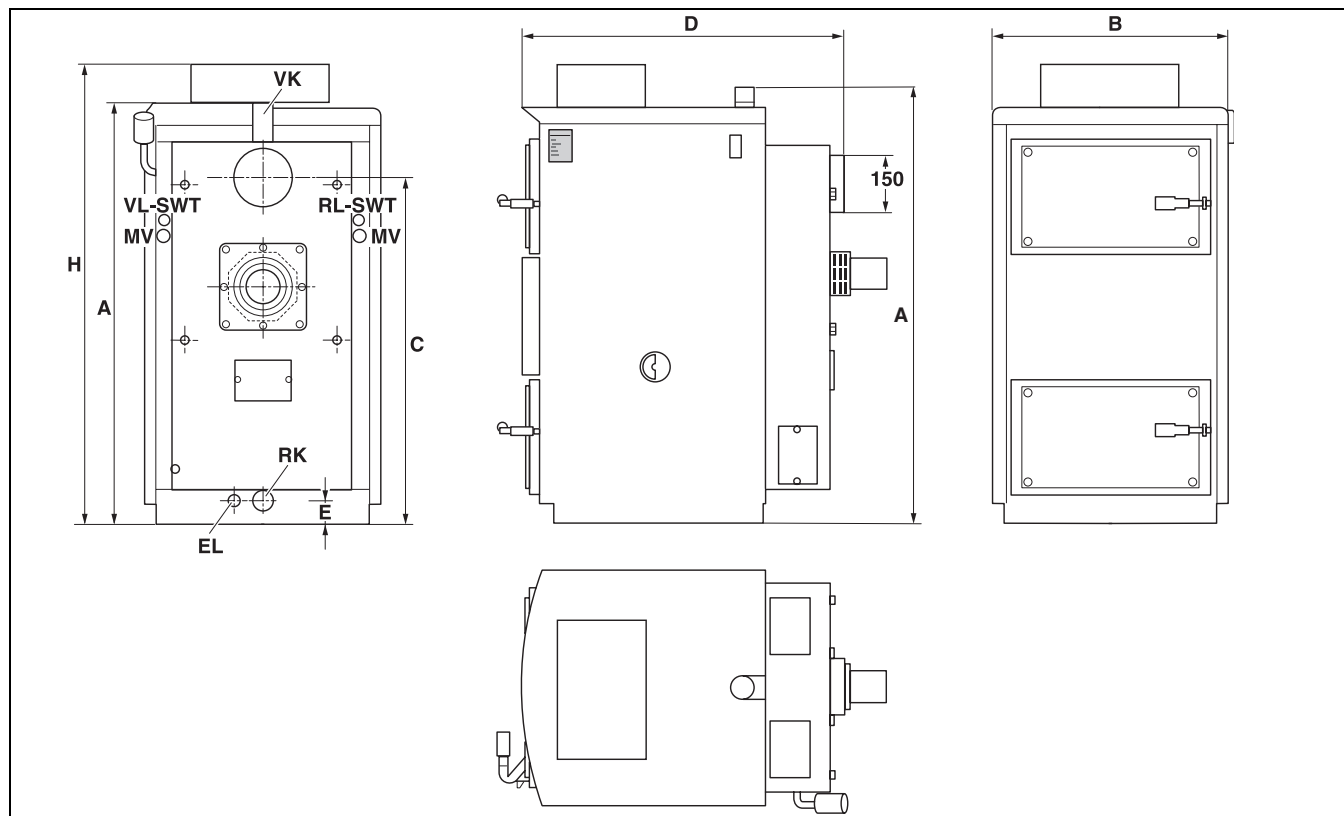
Racorduri și dimensiuni (dimensiuni în mm)
